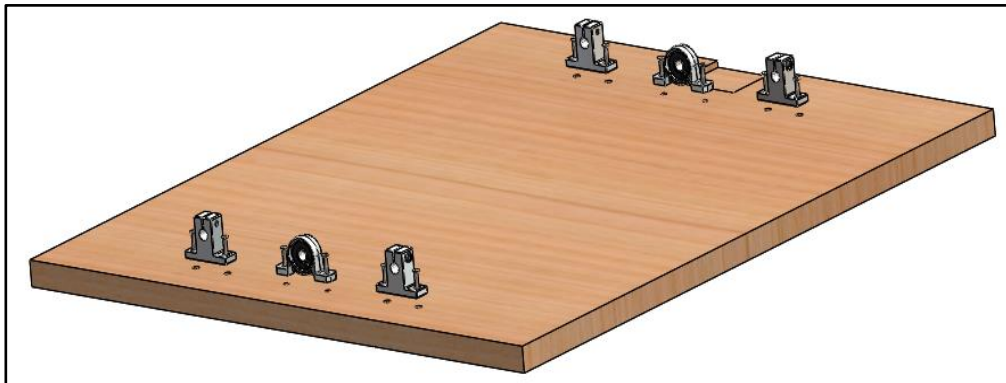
Vista isométrica del posicionamiento de los componentes mecánicos a la base eje X
